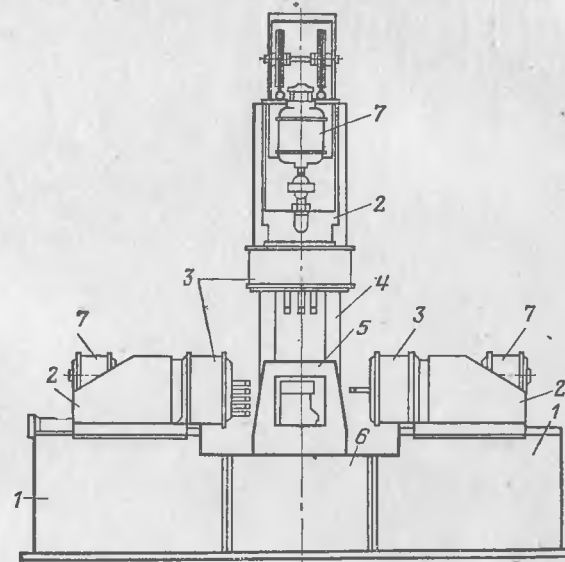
Общий вид трехстороннего агрегатного сверлильного станка.
